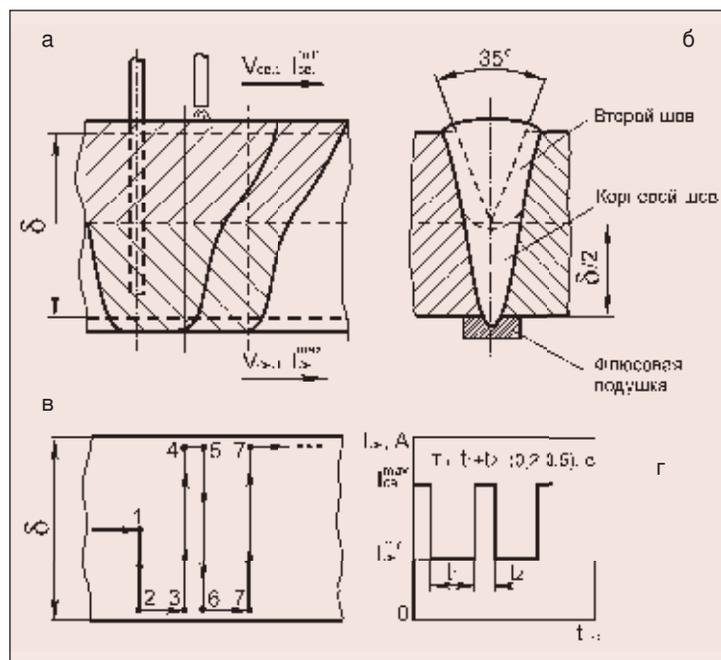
Способ сварки толстостенных изделий с регулированием параметров режима: а, в — порядок заполнения разделки электродным металлом (1–7 — местоположения электрода в процессе сварки); б — внешний вид сварного соединения; г — характер изменения силы сварочного тока
